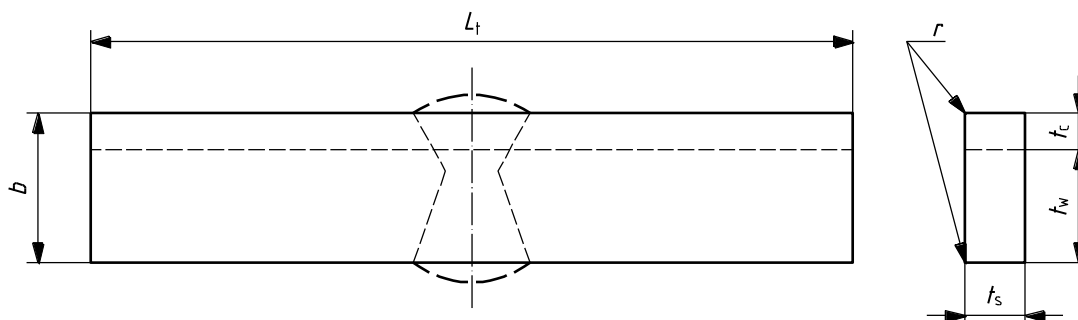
Образец для испытаний на загиб с растяжением боковой стороны для плакировки со стыковым сварным швом (SBCB)
